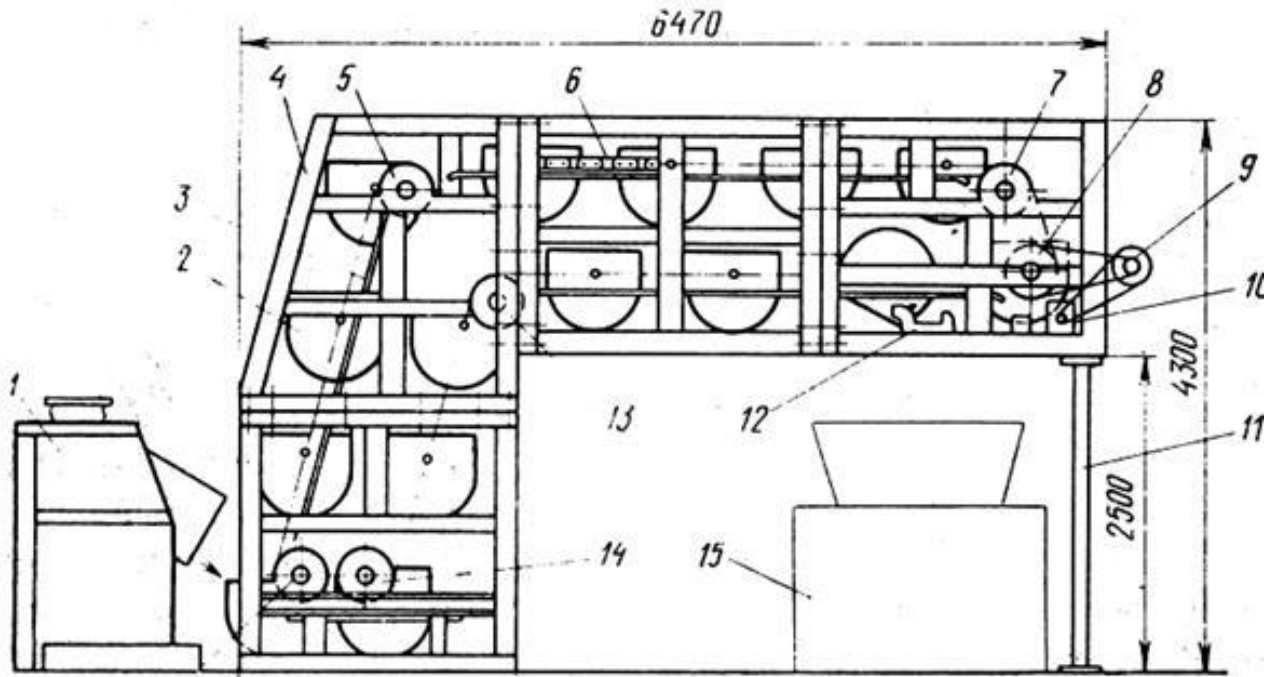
Ковшовий ланцюговий конвеєр Ш2-ХББ: тістомісильна машина; 2 – ємкості; 3 – напрямні, 4 – каркас; 5, 7, 13, 16 – зірочки; 6 – втулково-роликові ланцюги; 8 – привідна пара зірочок; 9 – проміжний вал; 10 – черв'ячний редуктор; 11 – стійки; 12 – механізм для повороту ємкості; 14 – натяжна пара зірочок; 15 – тістоподільник.
